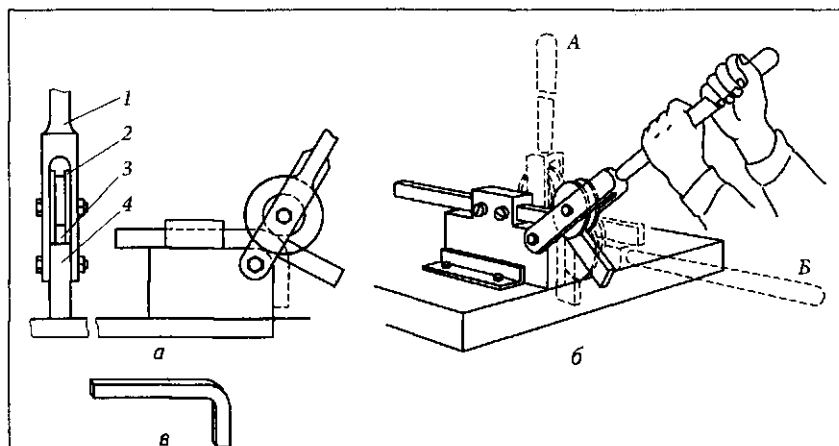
Приспособление для гибки рамки ножовочного станка:
